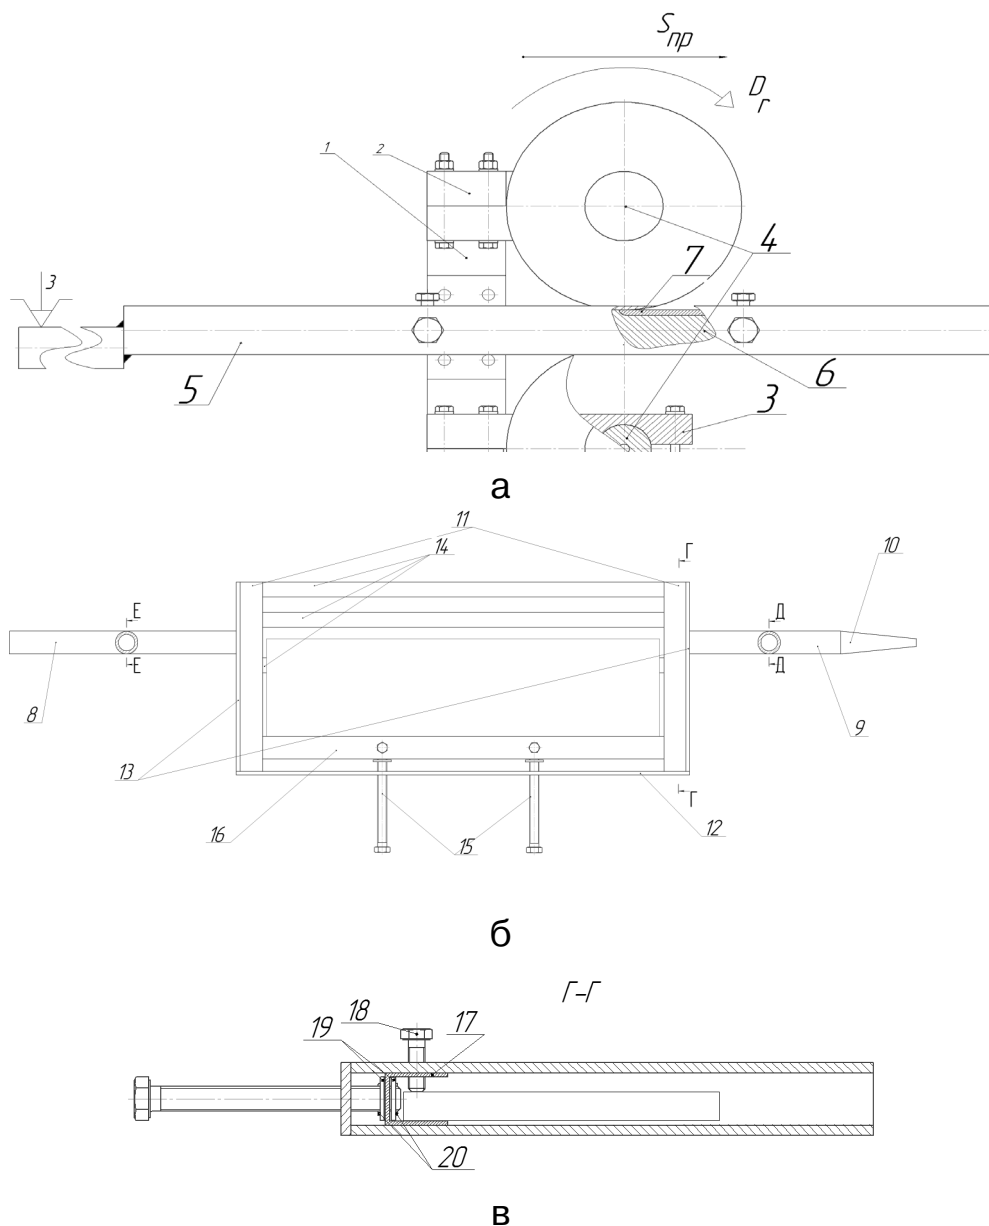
Устройство для электроконтактной приварки плоских поверхностей:
